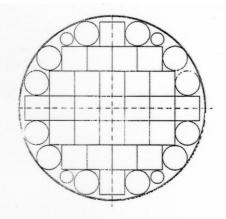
Схема раскроя крупногабаритной заготовки на отдельные режущие пластины различной формы.
